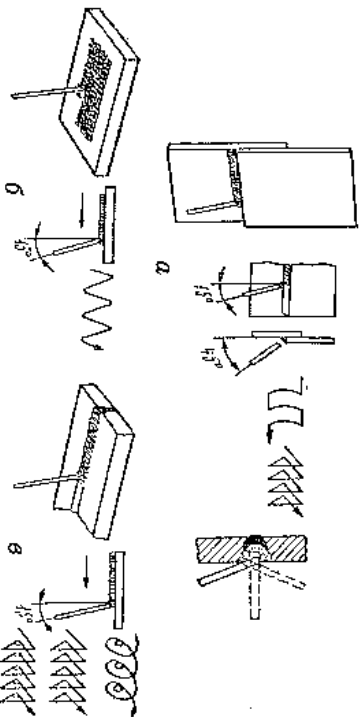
Положение и движения электрода при сварке в горизонтальном и потолочном положениях: а — горизонтальный угловой шов, б — наплавка в потолочном положении, в — потолочный стыковой шов
